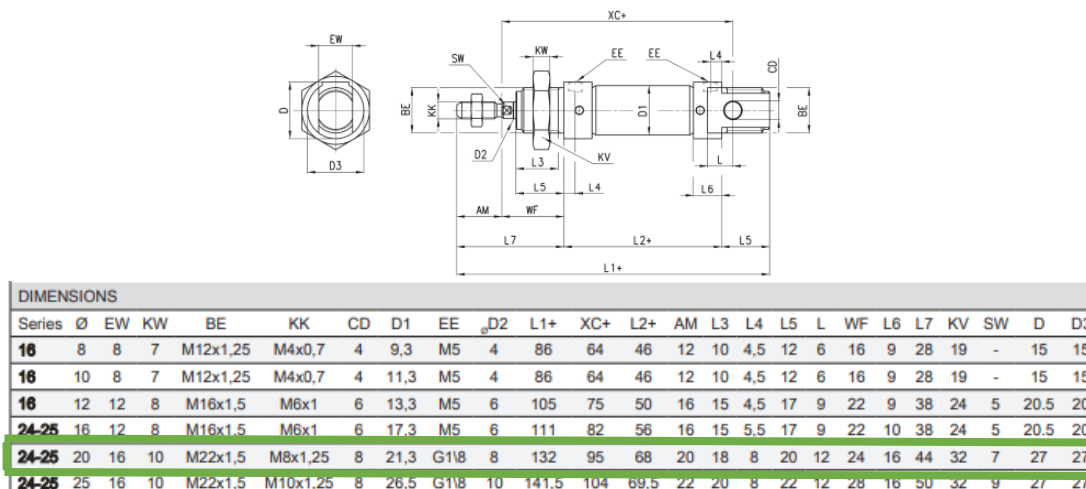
Dimensiones del minicilindro carrera de 150 mm. [18]
